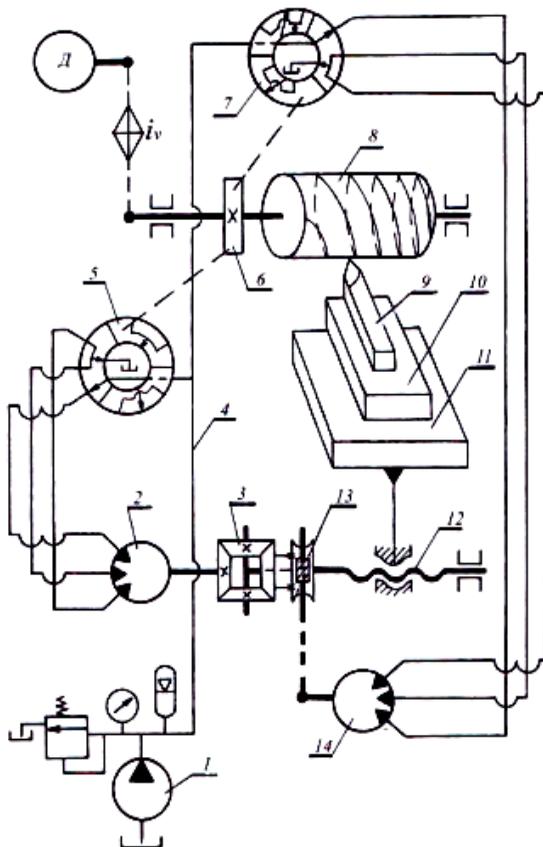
Структурная схема резьбонарезного станка с гидравлическими внутренними связями для нарезания цилиндрических винтовых поверхностей переменного шага
